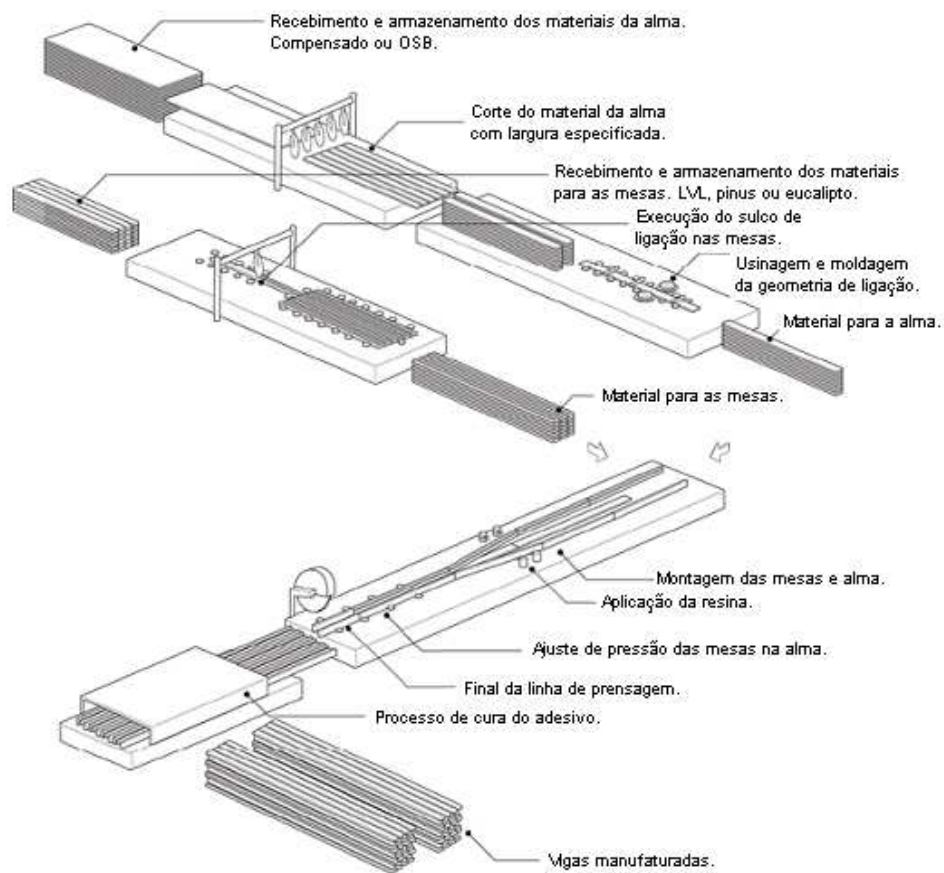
Modelo de fabricação de vigas em perfil "I"
